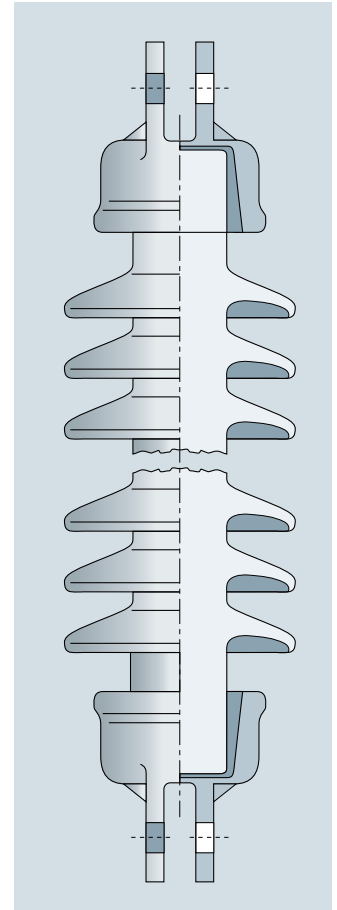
Aislador compuesto reforzado con fibra de vidrio con bola y accesorios de enchufe (aislante lapp)
